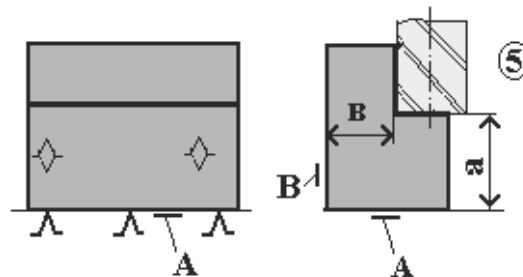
Пример *неполной схемы базирования* призматической заготовки.
